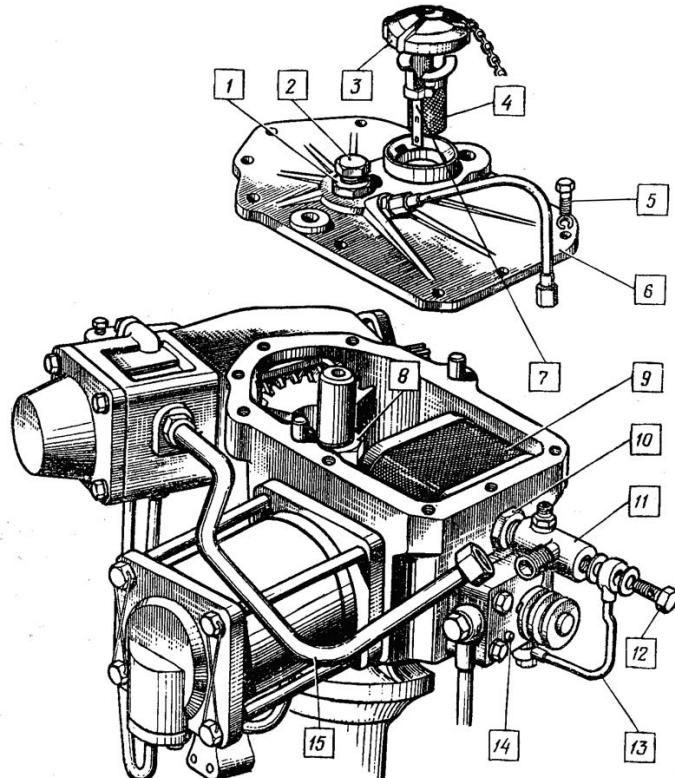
Гидроусилитель рулевого управления: 1, 10 — контргайки; 2 — регулировочный болт; 3 — крышка заливной горловины; 4 — фильтр; 5, 12 — болты; 6 — крышка; 7 — масломер; 8 — гайка; 9 — сливной фильтр; 11 — клапан; 13 — маслопровод клапана; 14 — щуп; 15, 16 — маслопроводы.
